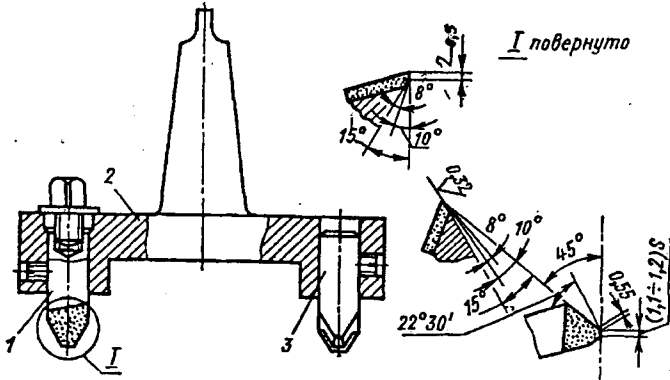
Однозуба фреза для обробки площин роз'єму вкладишів.
